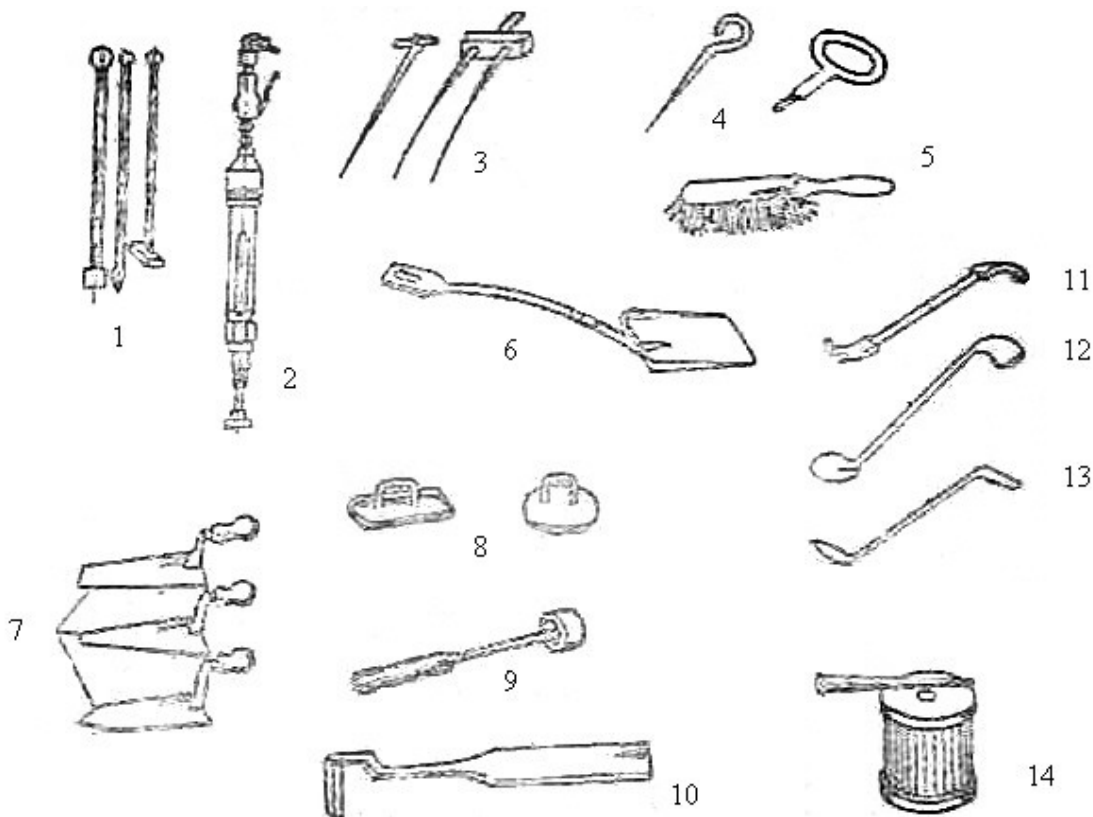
Інструмент для виготовлення ливарних форм:
